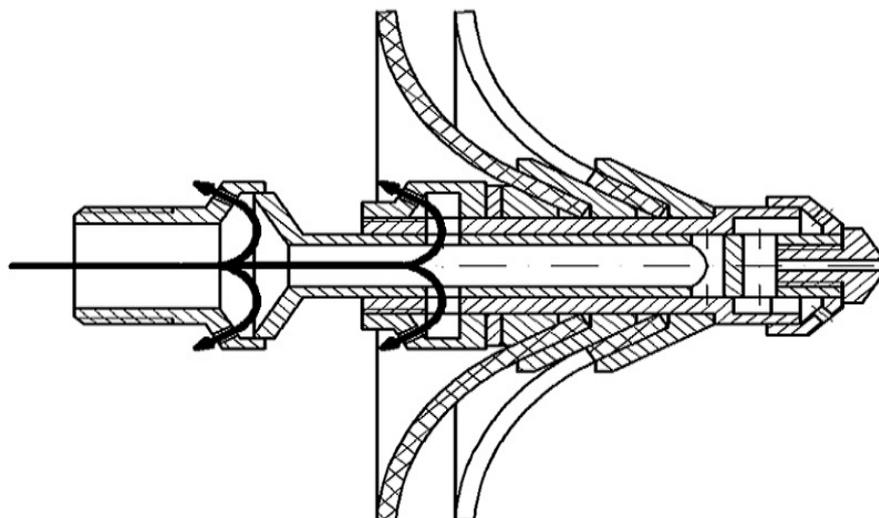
Конструкция реверсивной насадки промывочной мягкой (РНПМ) при ее извлечении из дренажного трубопровода
